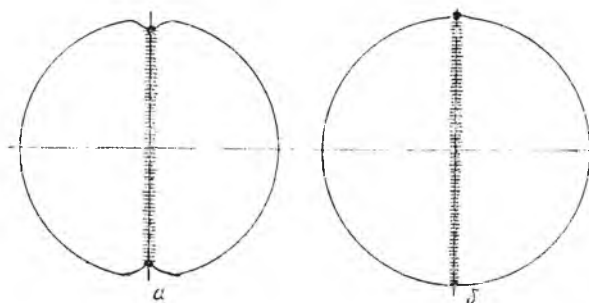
Характер остаточных перемещений тонкой сферической оболочки при сварке экваториальных швов: а — стальные и титановые оболочки; б — оболочки из алюминия
